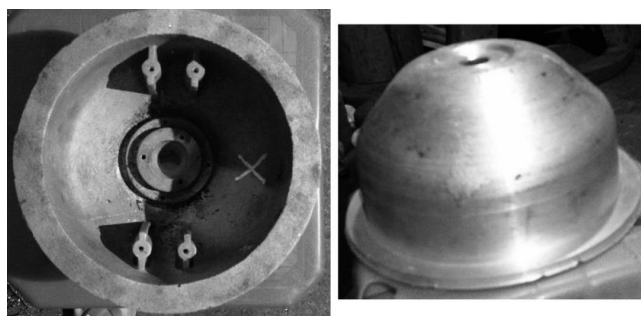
Вид внешнего корпуса Репитера и индикаторного механизма
